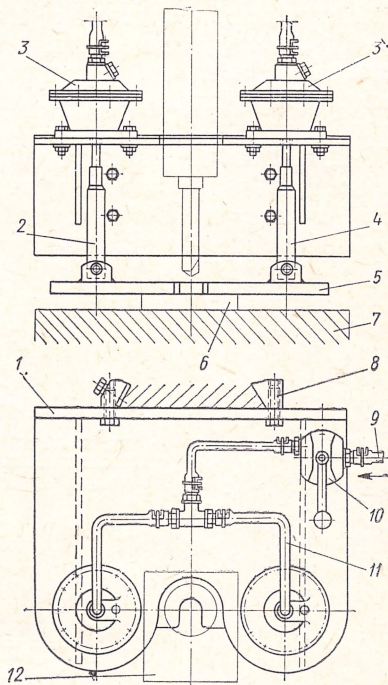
Приспособление для безопасного крепления детали на сверлильном станке
